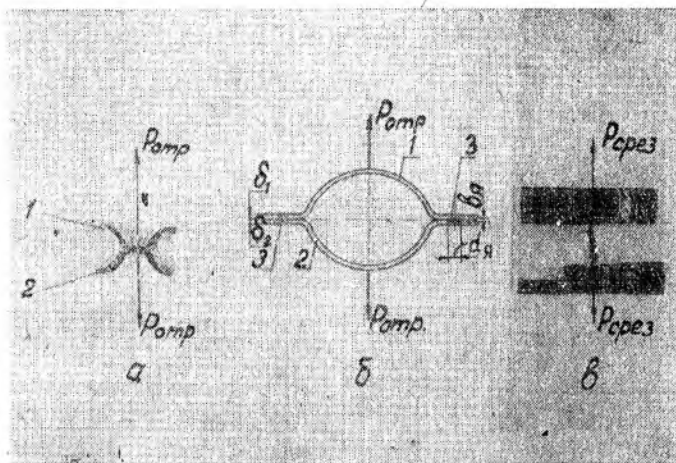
Схемы испытания сварных односточечных соединений а) на отрыв — односточечные образцы; б) на отрыв — двухточечные образцы; в) на срез
